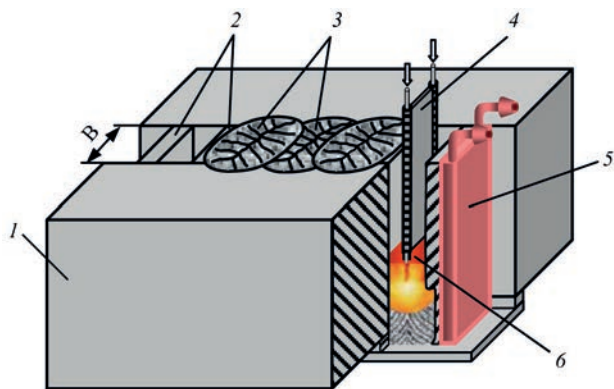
Схема способу БЕШЗ ПМ масивних виробів з великим перетином з'єднувальних елементів: 1 – зварювана деталь; 2 – формуючі перегородки; 3 – зварні шви; 4 – плавкий мундштук; 5 – охолоджуваний водою формуючий пристрій; 6 – шлакова ванна; В – зварювальний проміжок
